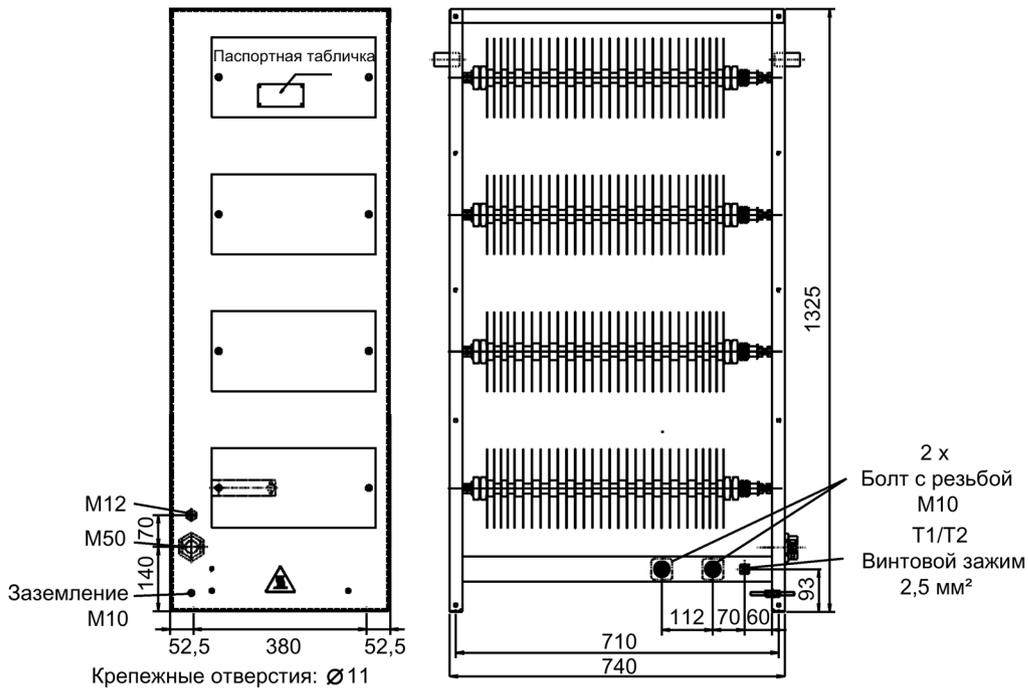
Габаритный чертеж тормозного резистора 50 кВт
